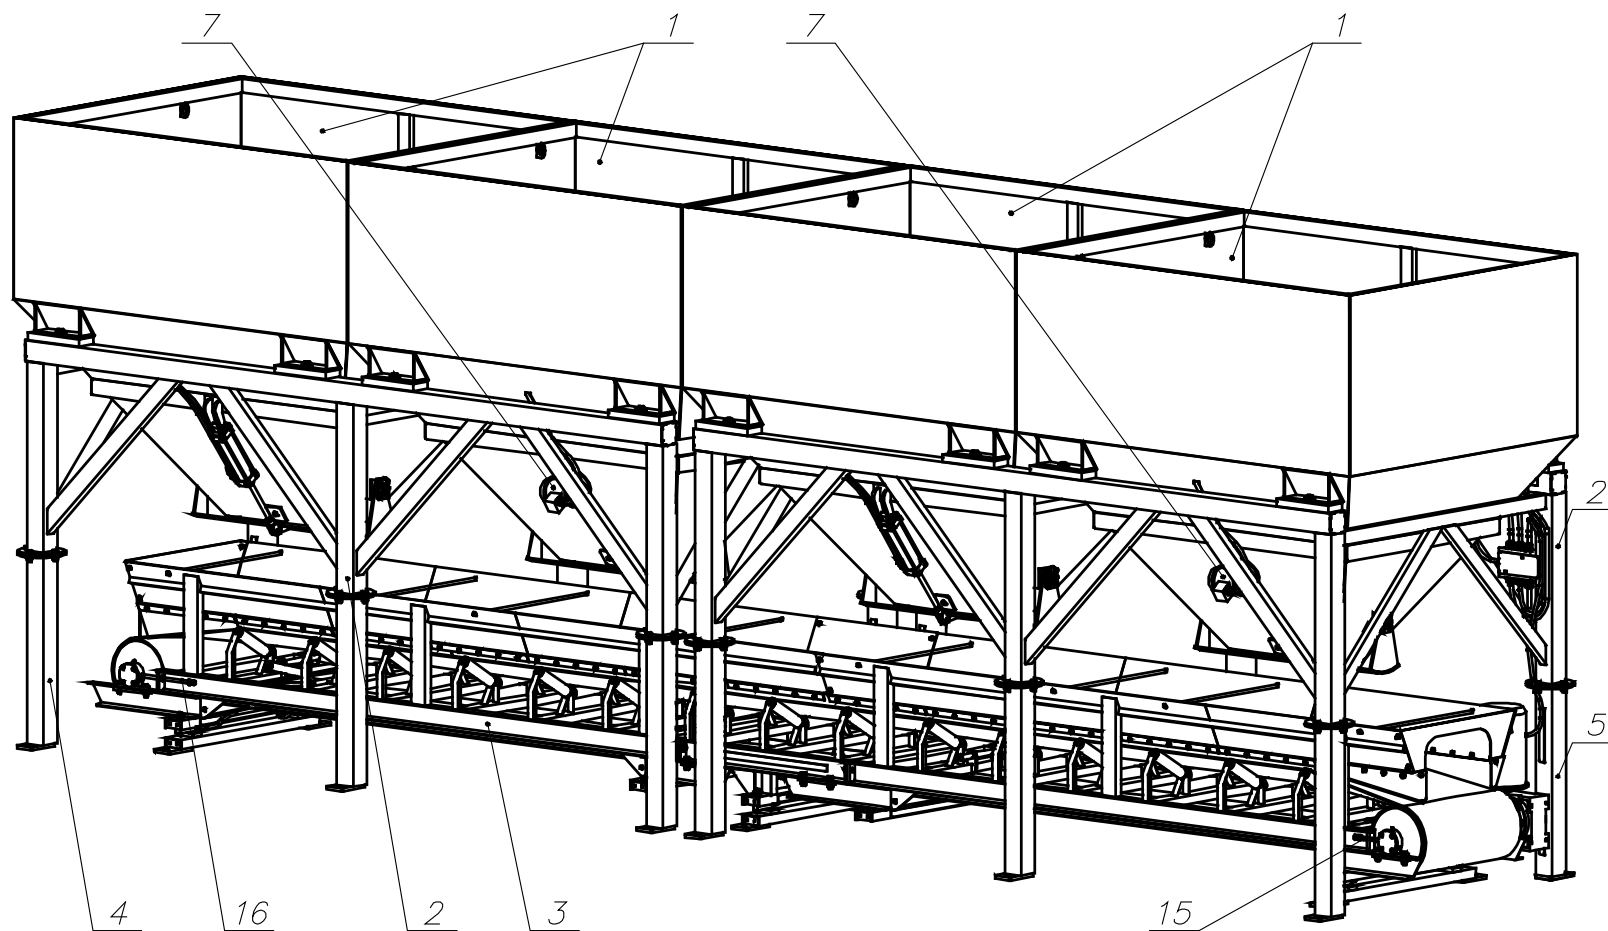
Общий вид дозатора ДЗ-28 вид спереди.
